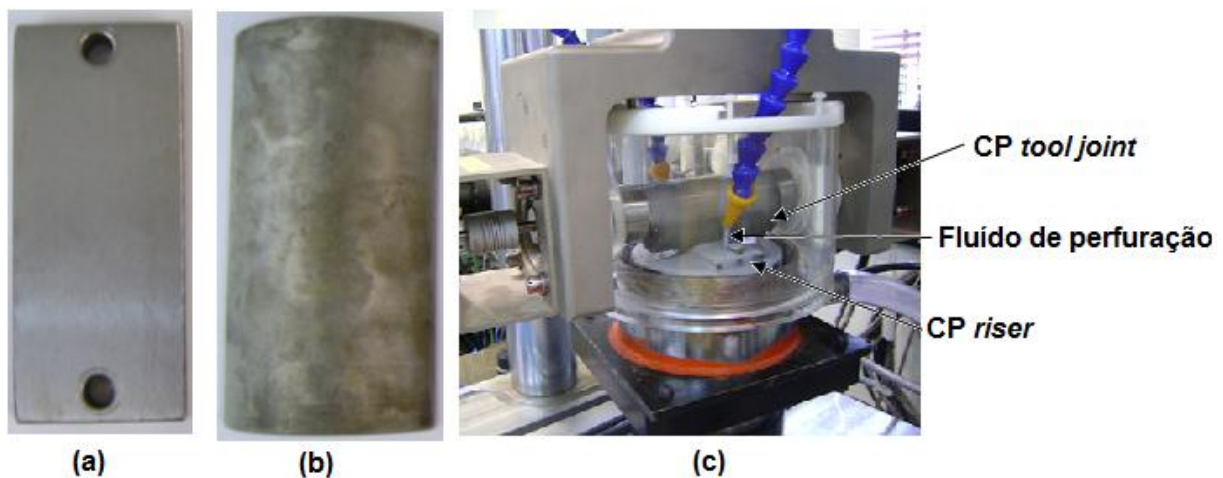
(a) CP riser (b) CP tool joint (c) montagem do ensaio de desgaste na MTS.
